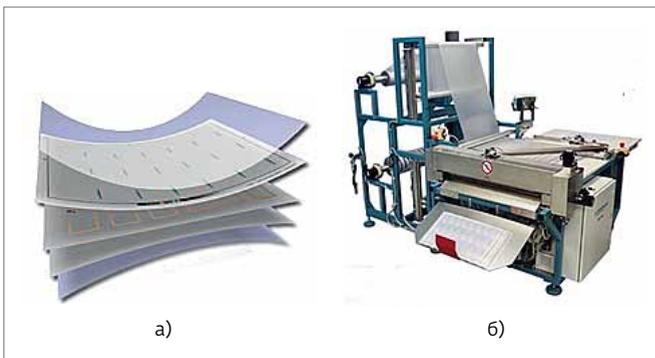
Сборка листов (а) и установка сборки SSC 200 (б)
